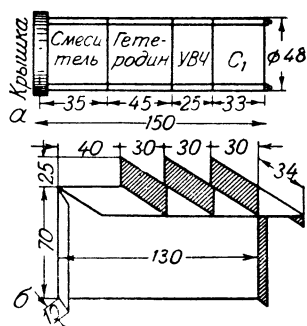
Конструктивные размеры шасси: а — для каскадов УВЧ, смесителя и гетеродина; б — для каскадов УПЧ, детектора, УНЧ и батарей
